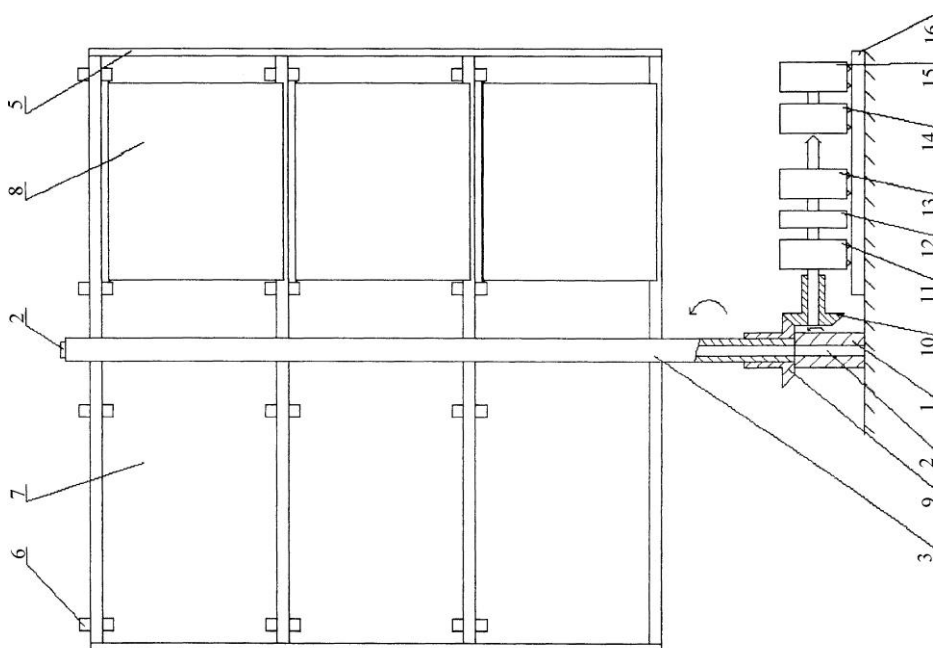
Вид сбоку конструкции ветроэнергетической установки
